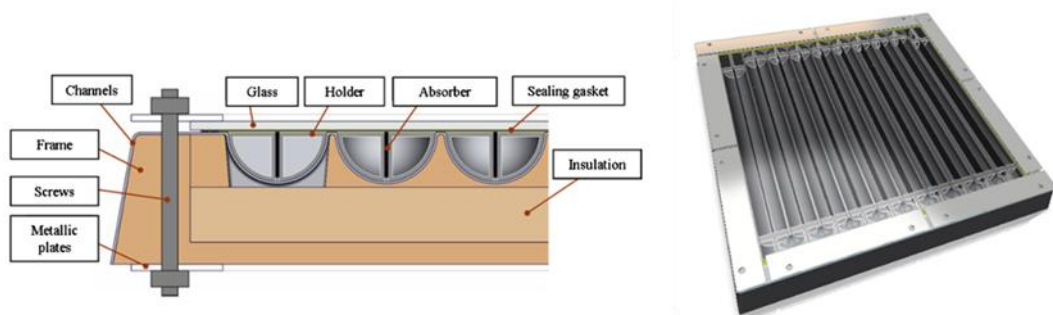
Corte transversal del diseño del segundo prototipo (izquierda) y diseño final del colector (derecha)
